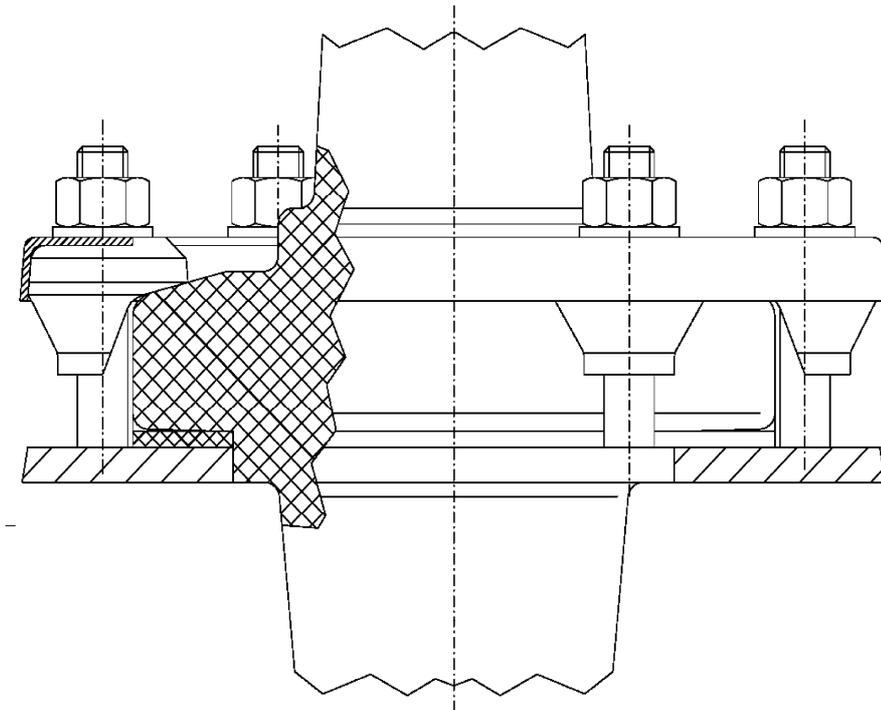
Befestigungsflansch und seine Befestigungsvorrichtung
